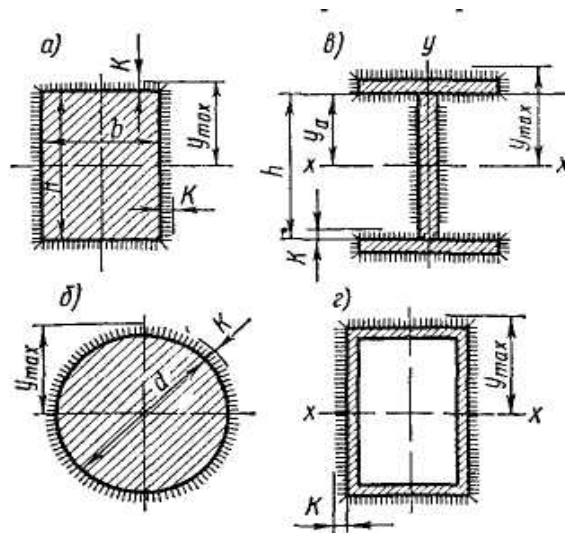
Зварні з'єднання елементів, обварених по периметрах кутовими швами:
